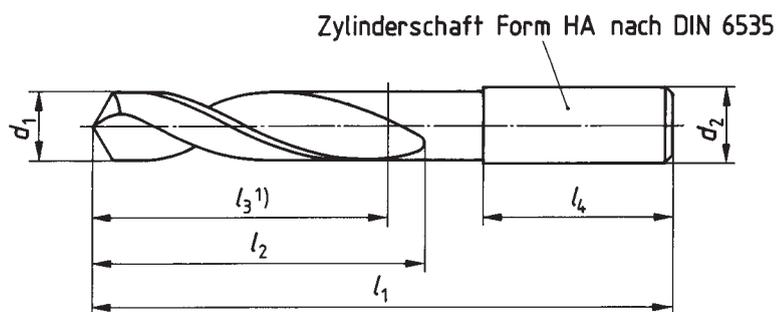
Zweischneidiger Vollhartmetall-Spiralbohrer
